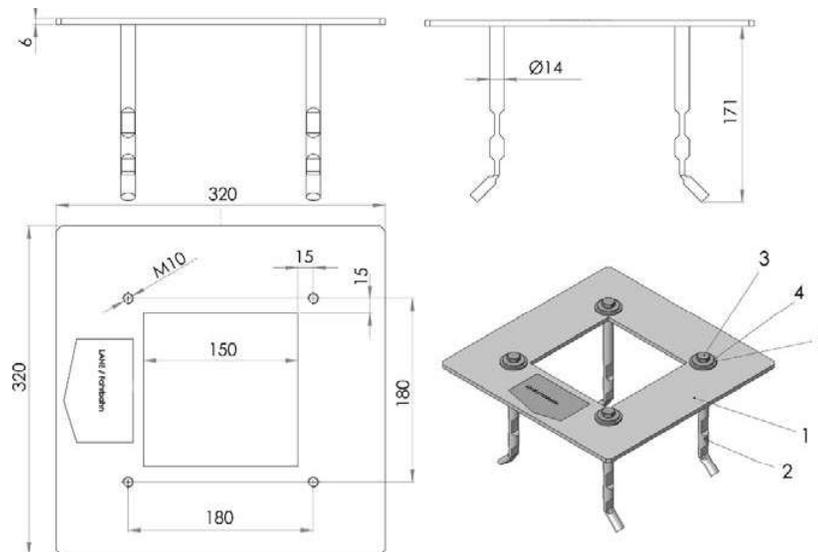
Platine de scellement PROACCESS (dimensions en mm)
